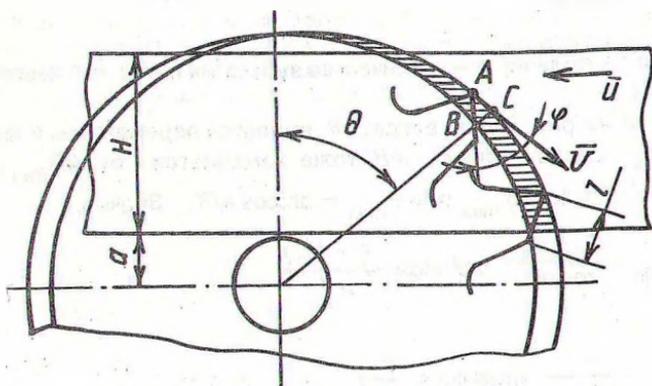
Формирование стенок пропила режущими зубьями при резании древесины универсальной круглой пилой
